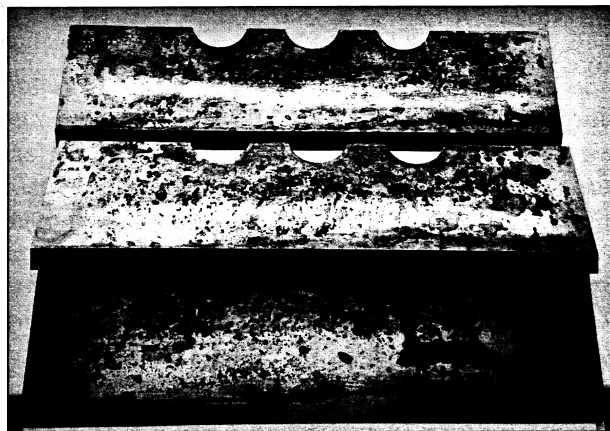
Опытные образцы ножей ФТИ5.001.1674 для рубки щепы
